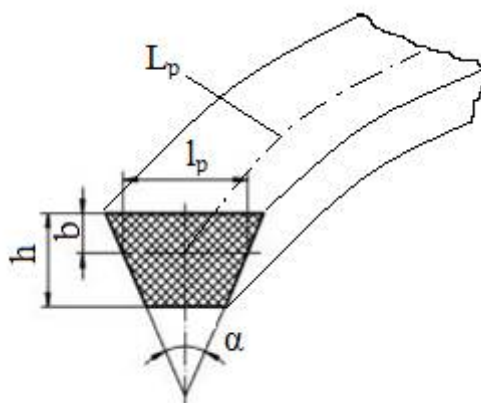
Elementele geometrice ale curelei trapezoidale [44]
